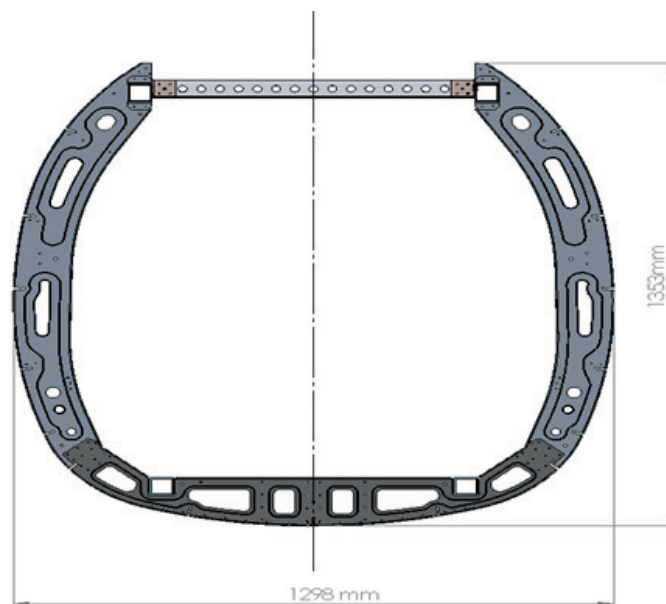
Dimensiones (mm) de la cadena de carga en vista frontal
